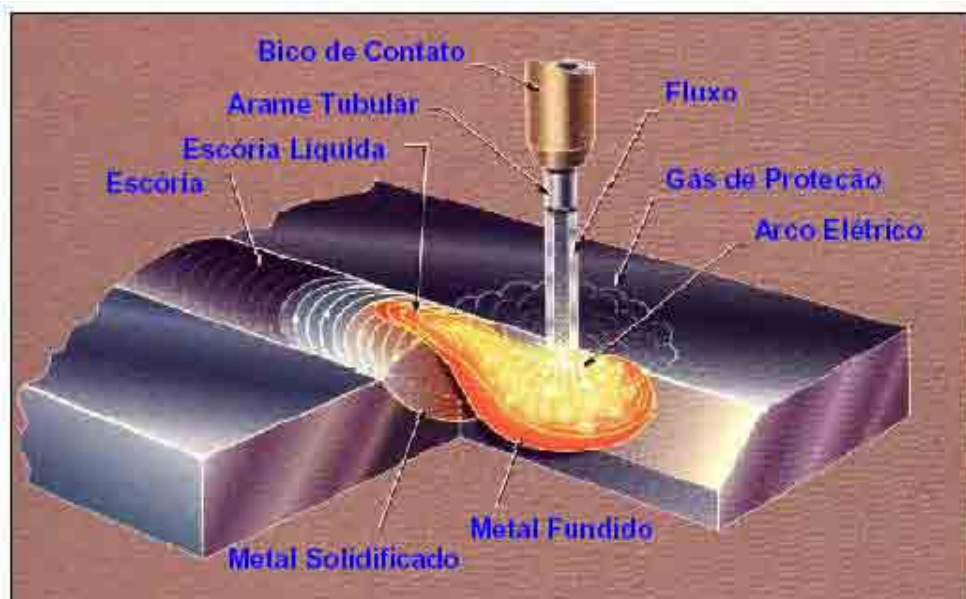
Esquema ilustrativo da soldagem com arame tubular autoprotetido (Fonte: Welding Handbook (1991)).
